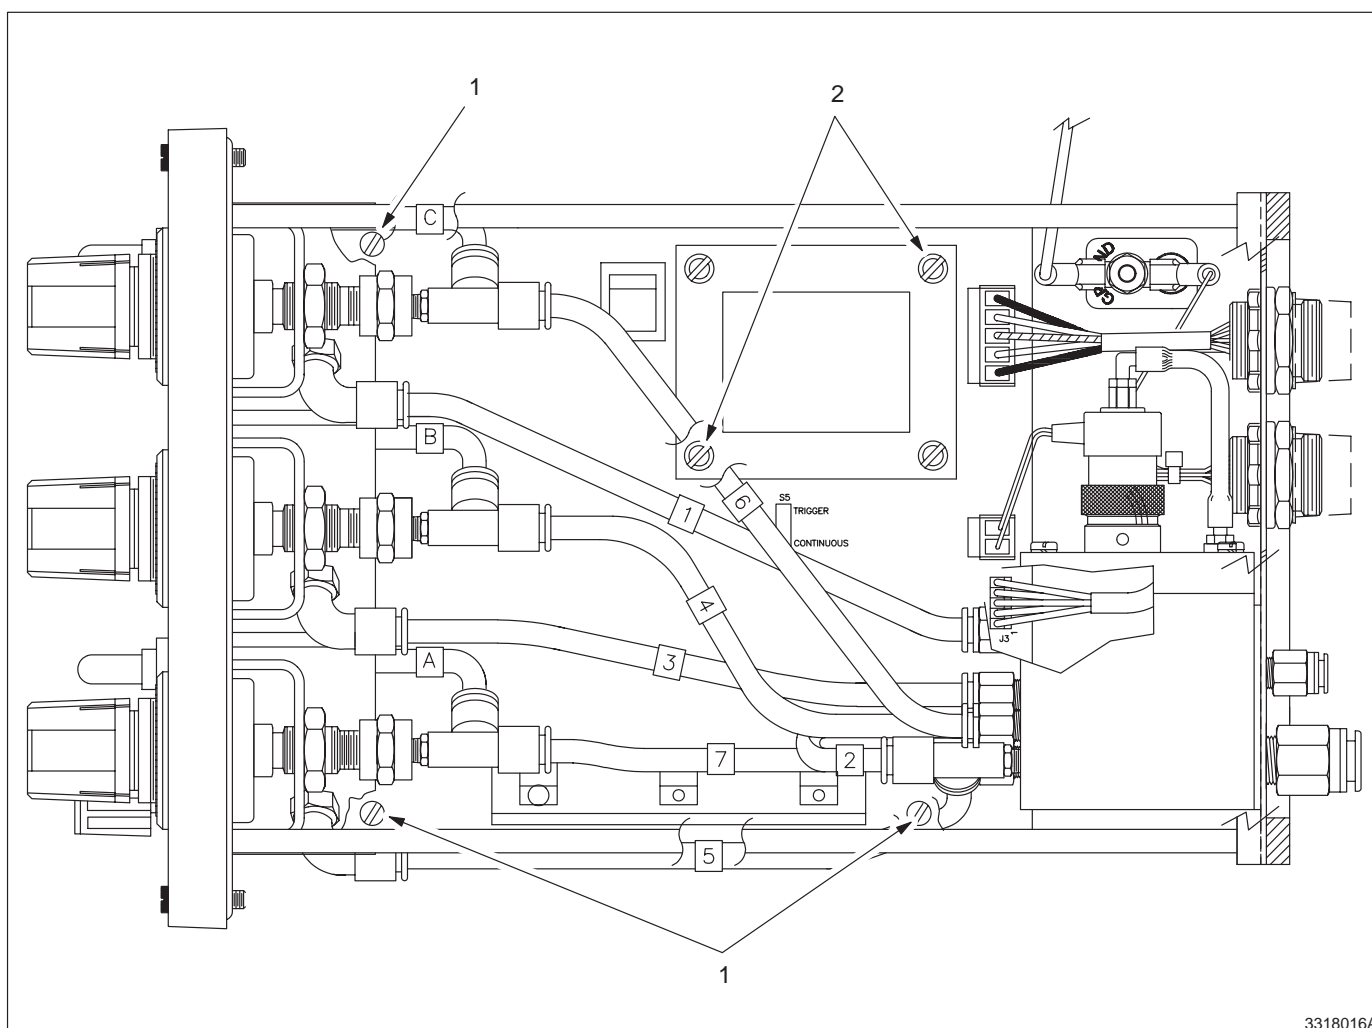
Entfernen der Platinen-Befestigungsschrauben
